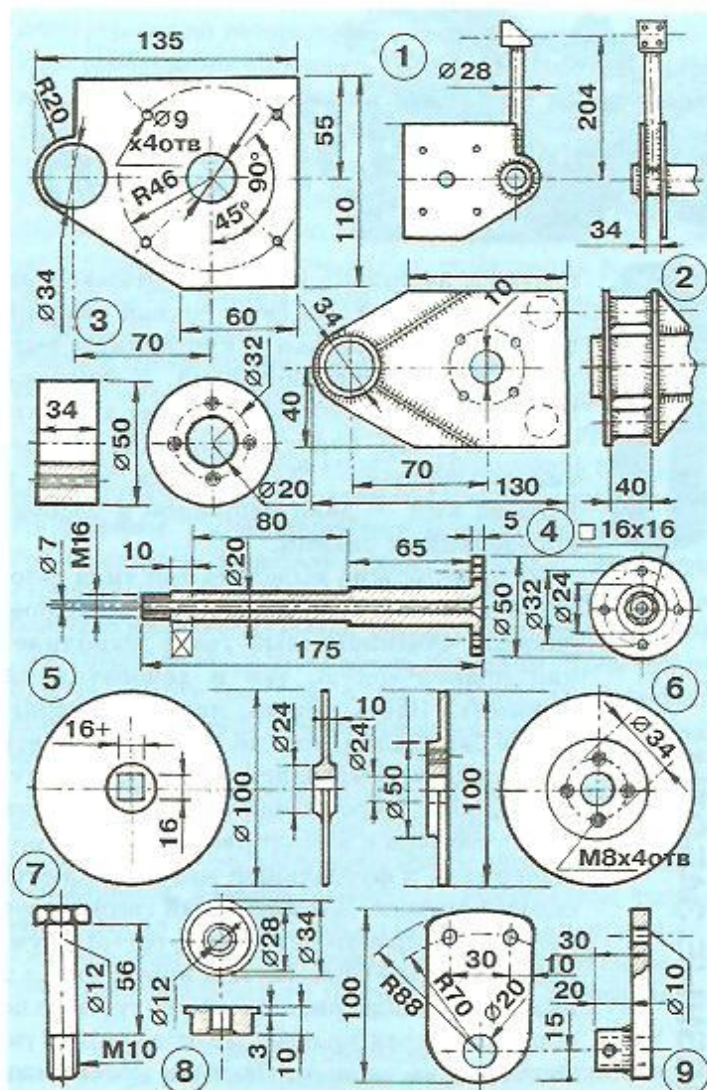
Детали карты: 1 — пластина кронштейна крепления УМУ; 2 — кронштейн крепления заднего колеса; 3 — втулка крепления оси ведущего колеса; 4 — ось ведущего колеса; 5 — диск для тормозных колодок ведущего колеса; 6 — диск для тормозных колодок (3 шт.); 7 — шкворень (2 шт.); 8 — втулка шкворня (бронза, 4 шт.); 9 — сошка руля.
